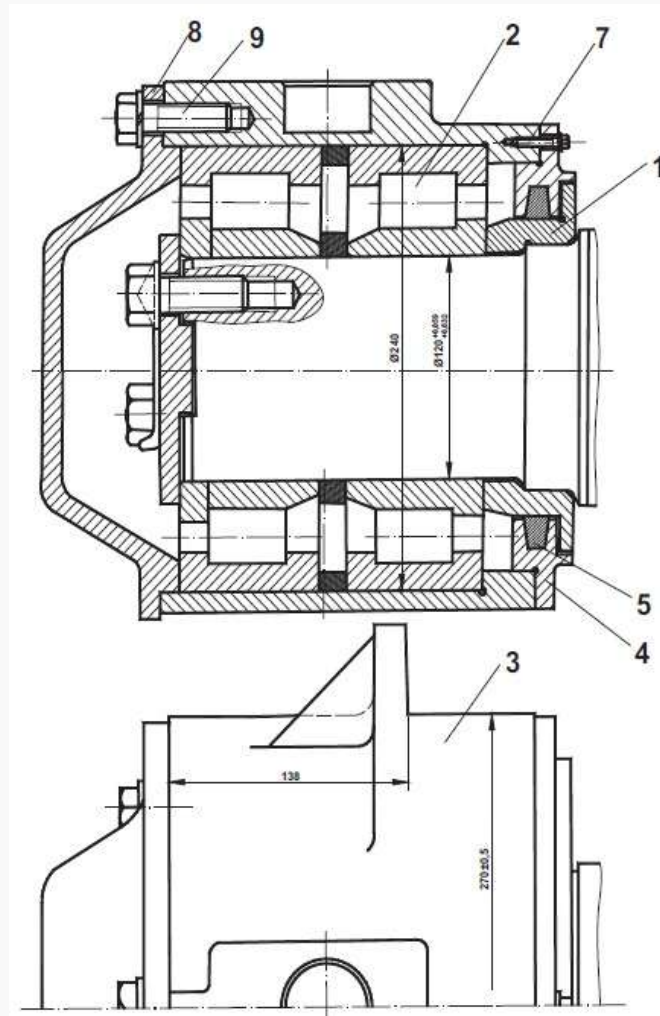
Cutie de osie din două bucăți pentru automotor pe două osii
